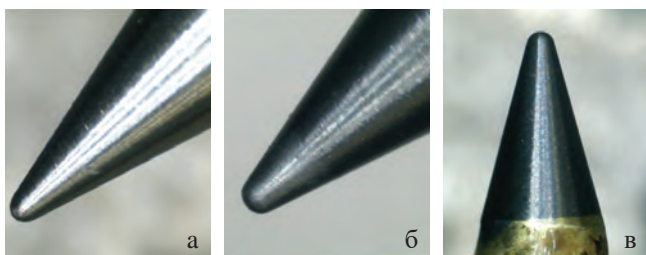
а – дорн прошлифованный и отполированный после обработки деталей из стали Х12М, б – дорн из инструментальной стали Р6М5, в – напайный дорн с напайным наконечником из стали Р6М5
